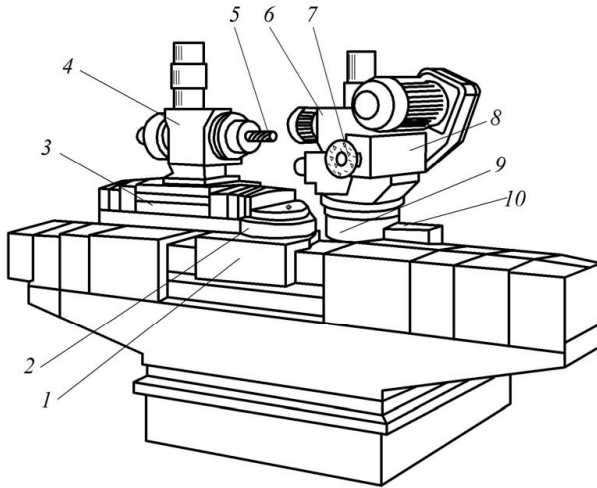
Конструкция шлифовально-заточного центра: 1 – продольные салазки; 2 – поворотная планшайба; 3 – ходовые салазки; 4 – бабка изделия; 5 – заготовка; 6 – неподвижная шлифовальная бабка; 7 – шлифовальный круг; 8 – поворотная шлифовальная бабка; 9 – поперечный суппорт; 10 – вертикальные салазки
